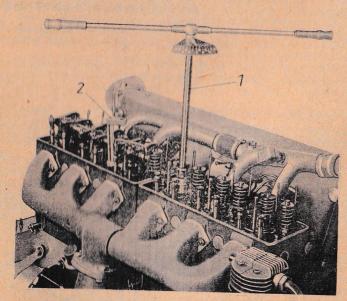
Anziehen der Muttern zur Befestigung des Zylinderkopfes
